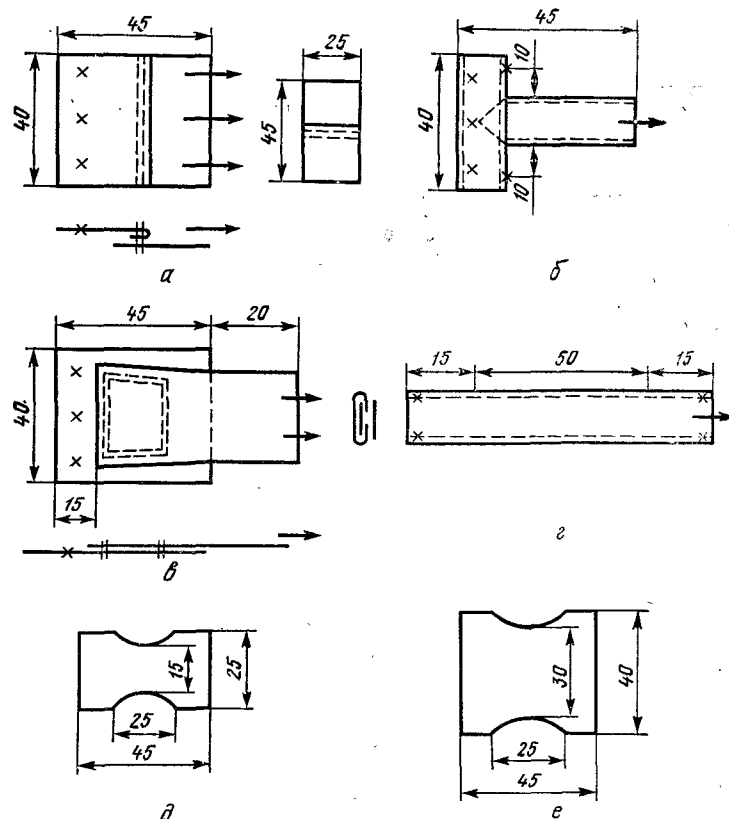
Форма и размеры простроченных образцов для определения прочности швов заготовок верха обуви (а), ремешков (б), продольных ремней (в) и ремешков (г), испытывающих наибольшее напряжение, и непростроченных образцов для задинки (д), союзки и берцов (е)
